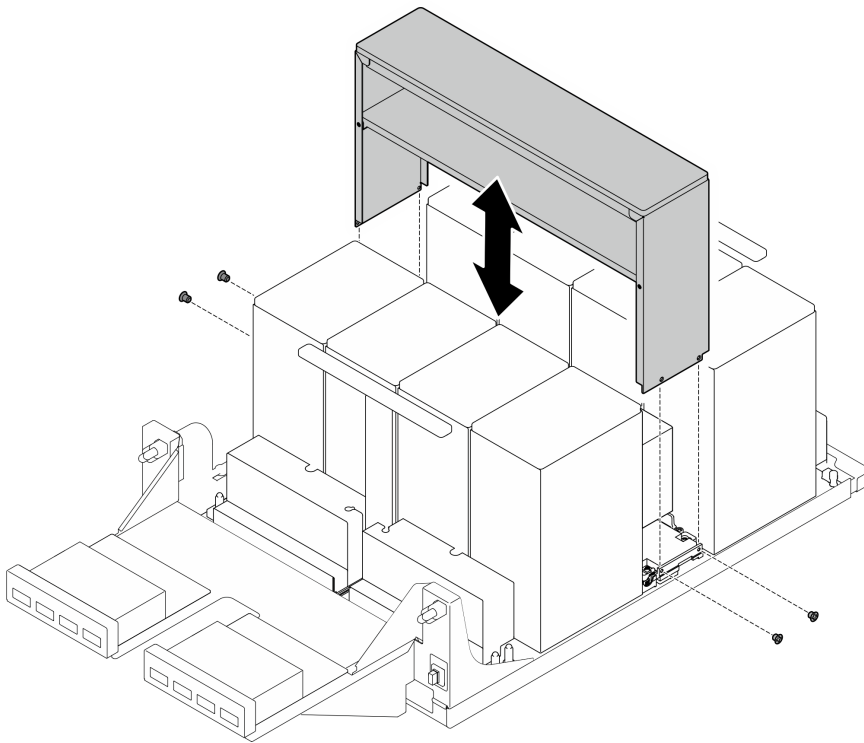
Installation du cache du dissipateur thermique NVSwitch
